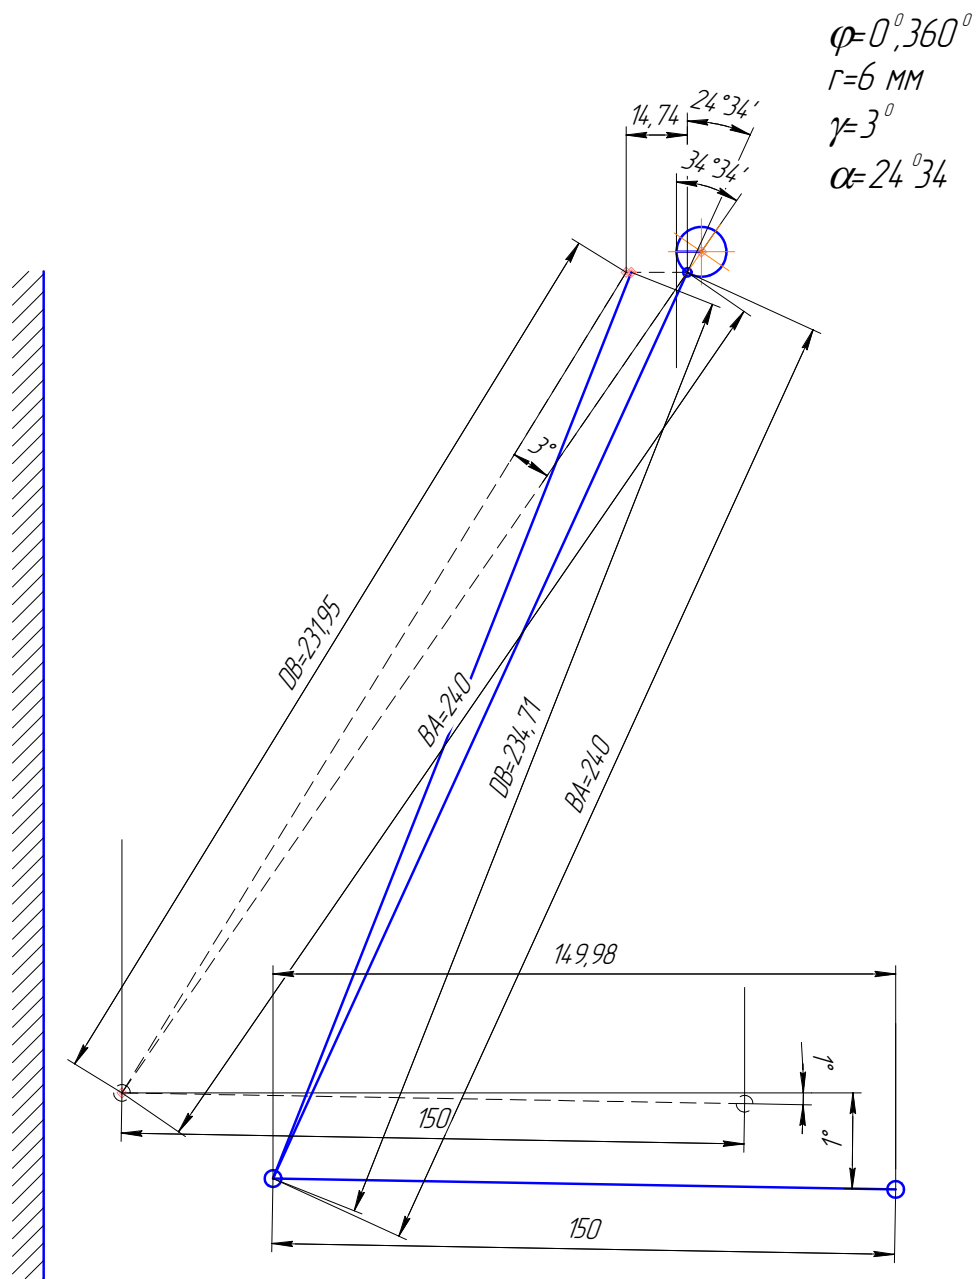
Розрахункова схема переміщення рухомої щоки
